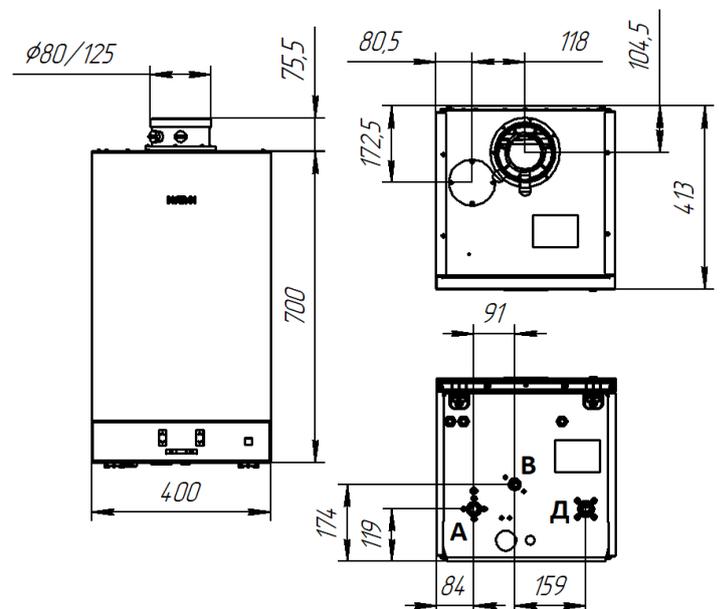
Габаритные и присоединительные размеры PC49-00.00/PC60-00.00
